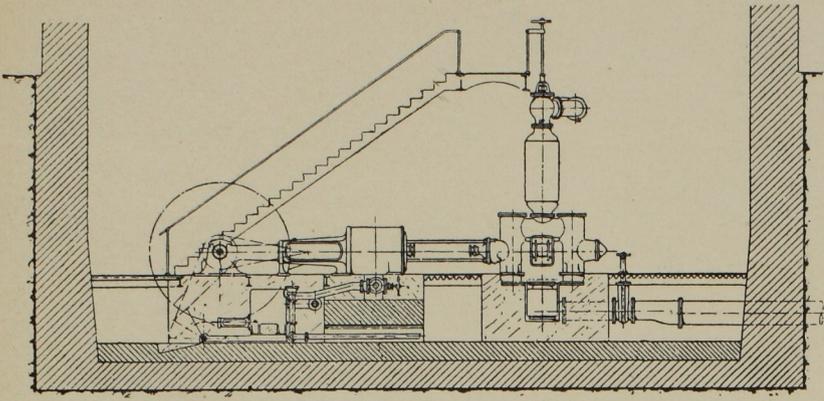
Seitenansicht der Pumpmaschine. Masst. 1 : 150.
